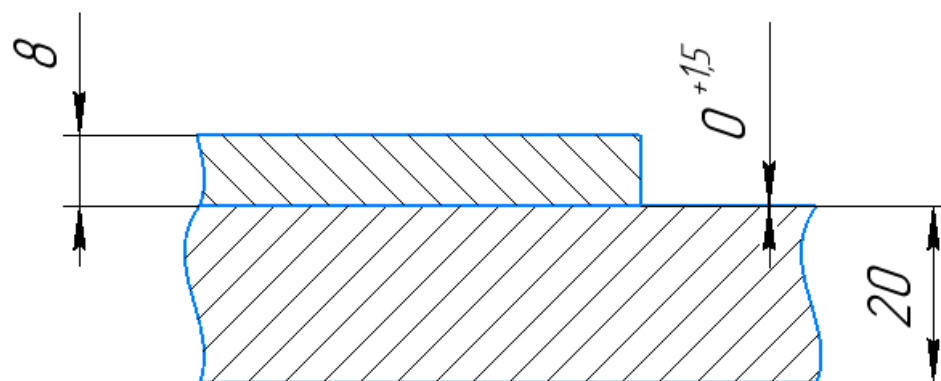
Подготовка кромок свариваемых деталей для типа сварного соединения Н1 по ГОСТ 5264-80
